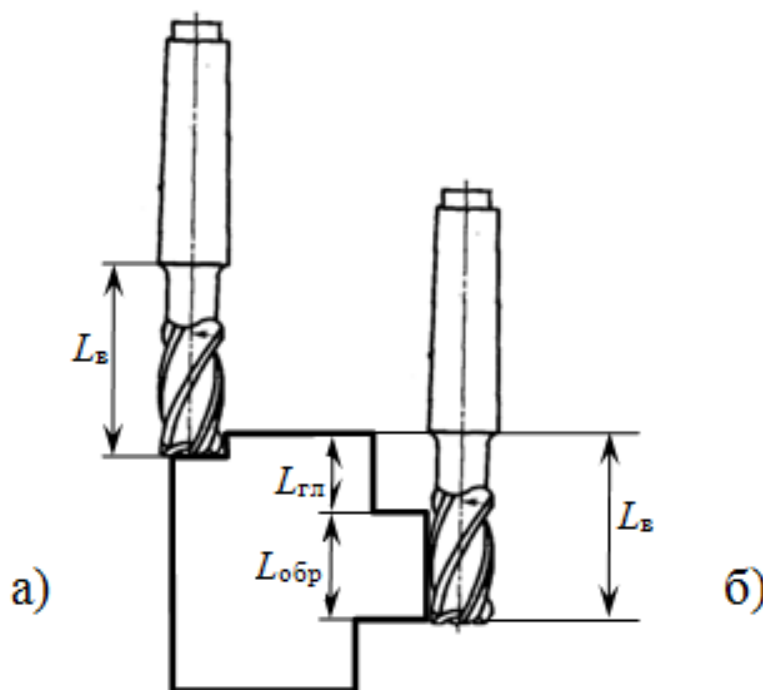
Схемы определения вылета фрезы: а – для поверхности, расположенной наверху заготовки, б – для заглубленной поверхности
